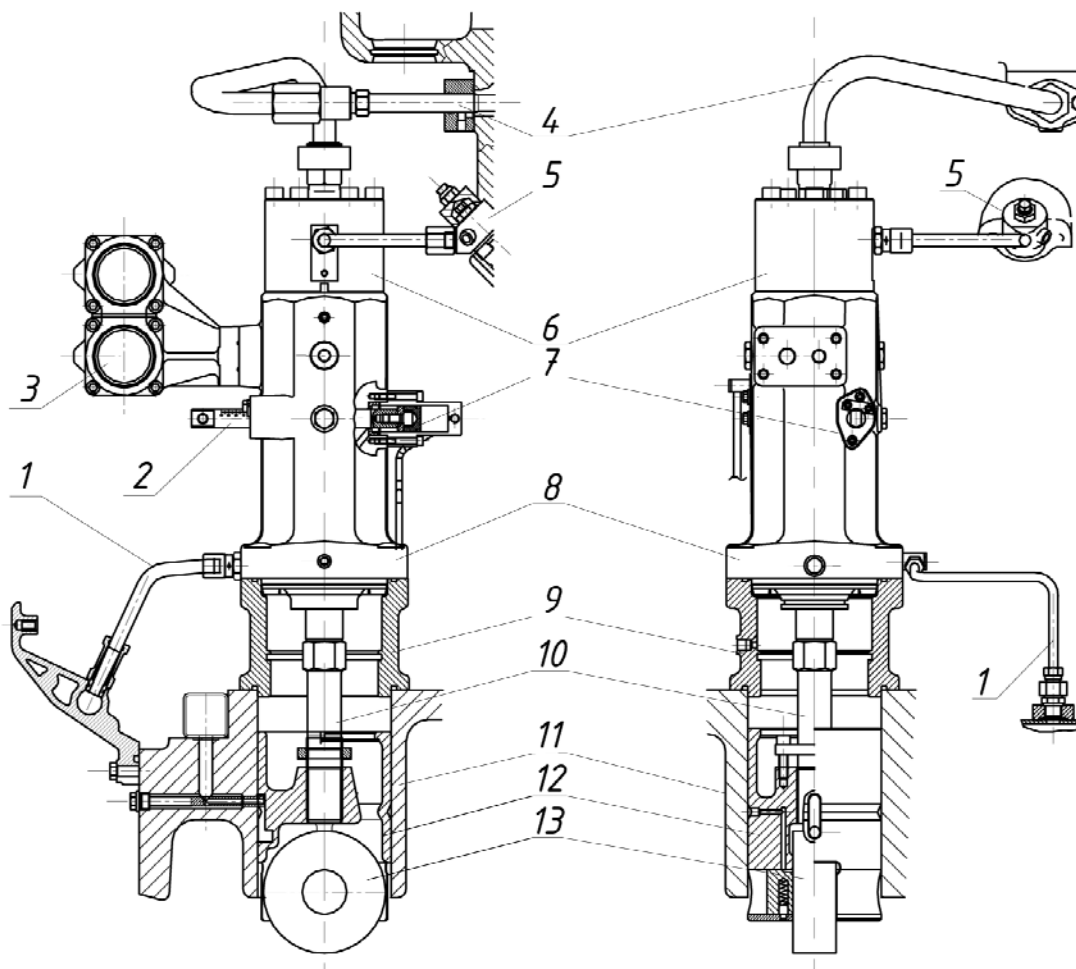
Приєднання паливних насосів: 1 – трубка зливу протічок; 2 – рейка; 3 – паливна магістраль низького тиску; 4 – паливна трубка високого тиску; 5 – форсунка запального палива; 6 – кришка ПНВТ; 7 – демпферний пристрій; 8 – корпус ПНВТ; 9 – проставка; 10 – штовхач; 11 – корпус штовхача; 12 – стакан штовхача; 13 – ролик приводу
